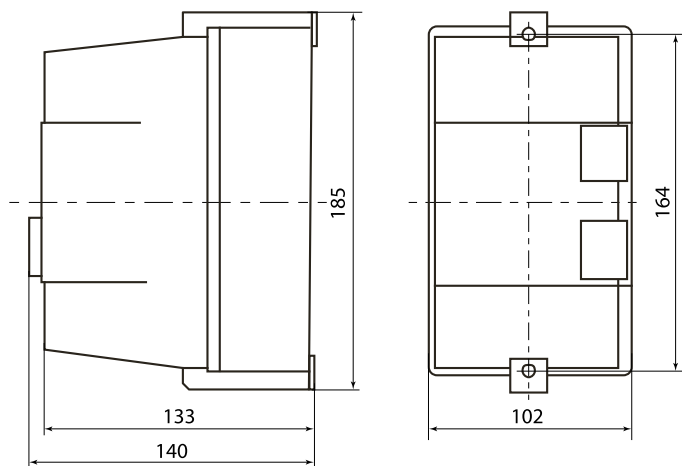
Габаритные размеры контакторов КМН 22560, КМН 23260, мм
